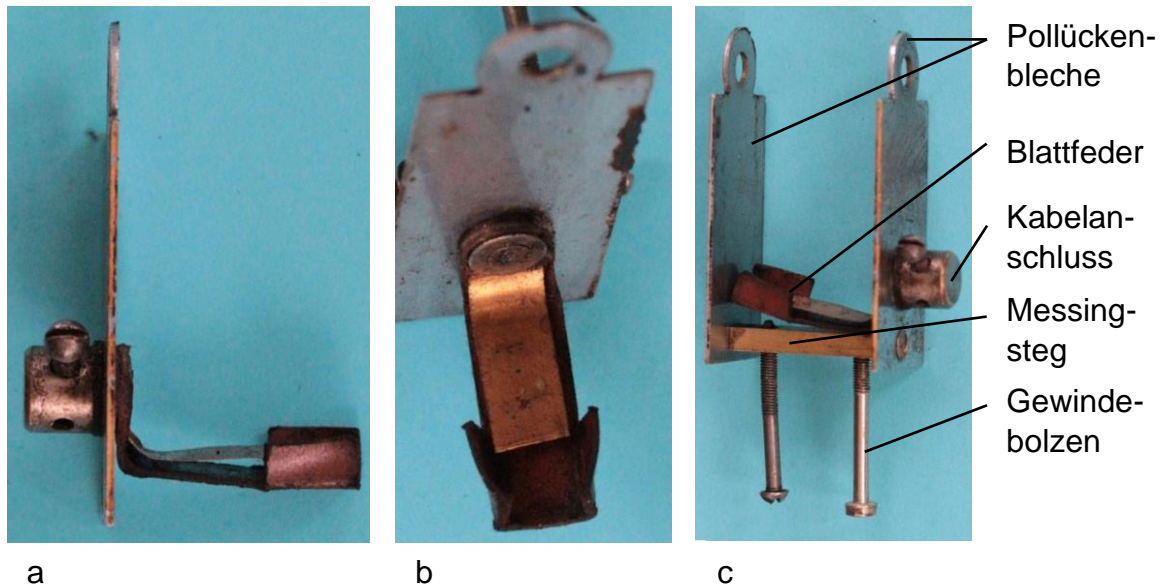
Spannung führender Kontakt: a) Pollückenblech mit Kabelanschlussklemme, (b) Pollückenblech mit Blattfeder, c) Verbindung der Pollückenbleche mit einem Messingsteg
